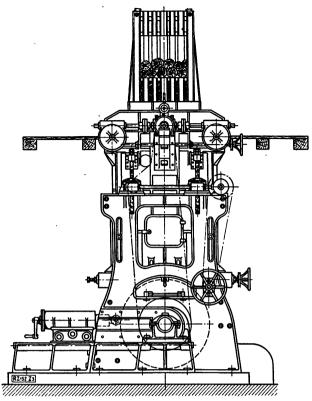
Einpressiger Großflächenschleifer, Bauart Füllner-Werk, Warmbrunn. Zum Vorschub des Holzes dienen Schraubenspindeln.
